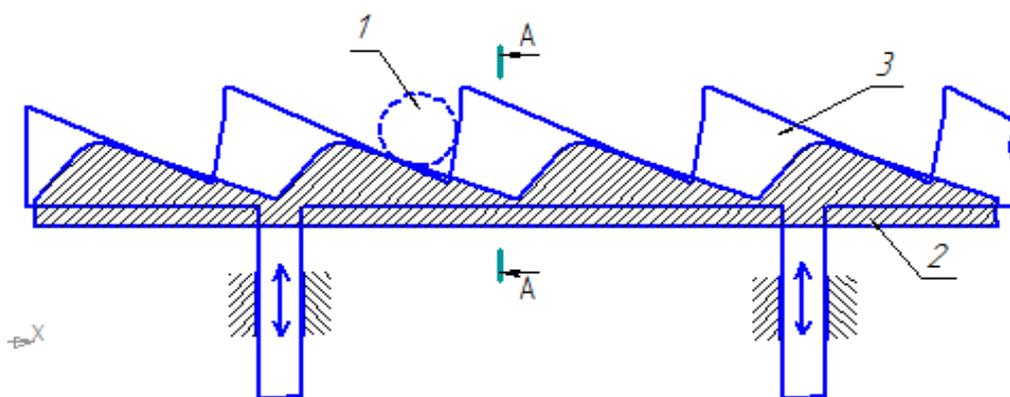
Устройство для перемещения круглых изделий в нагревательной печи: 1 – нагреваемое изделие; 2 – неподвижная шагающая балка; 3 – подвижная шагающая балка
